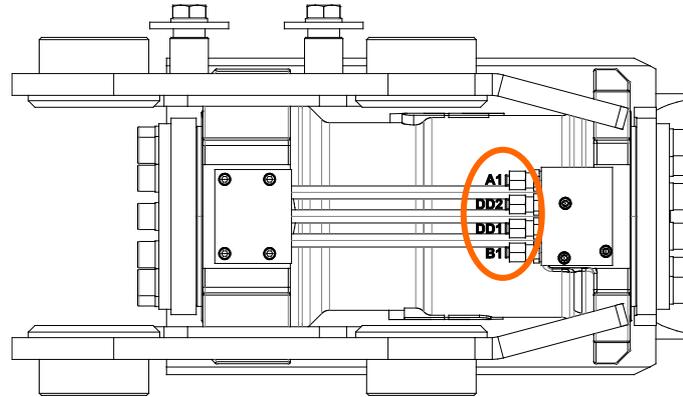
Rädlinger Tilt 90 mit Collecting Unit
